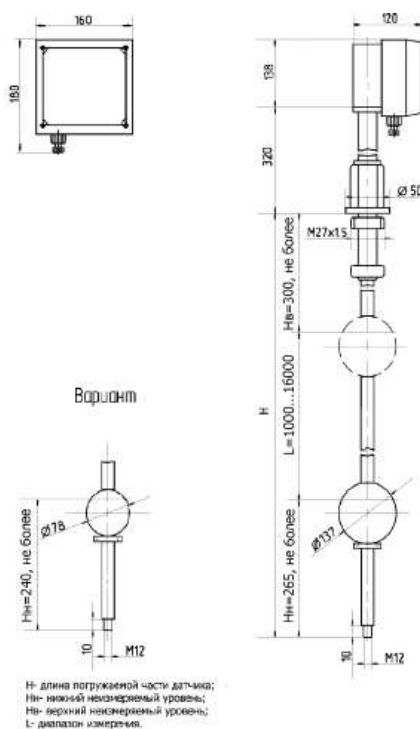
Габаритные и присоединительные размеры преобразователя (ПП) для измерения уровня двух несмешивающихся жидких сред
